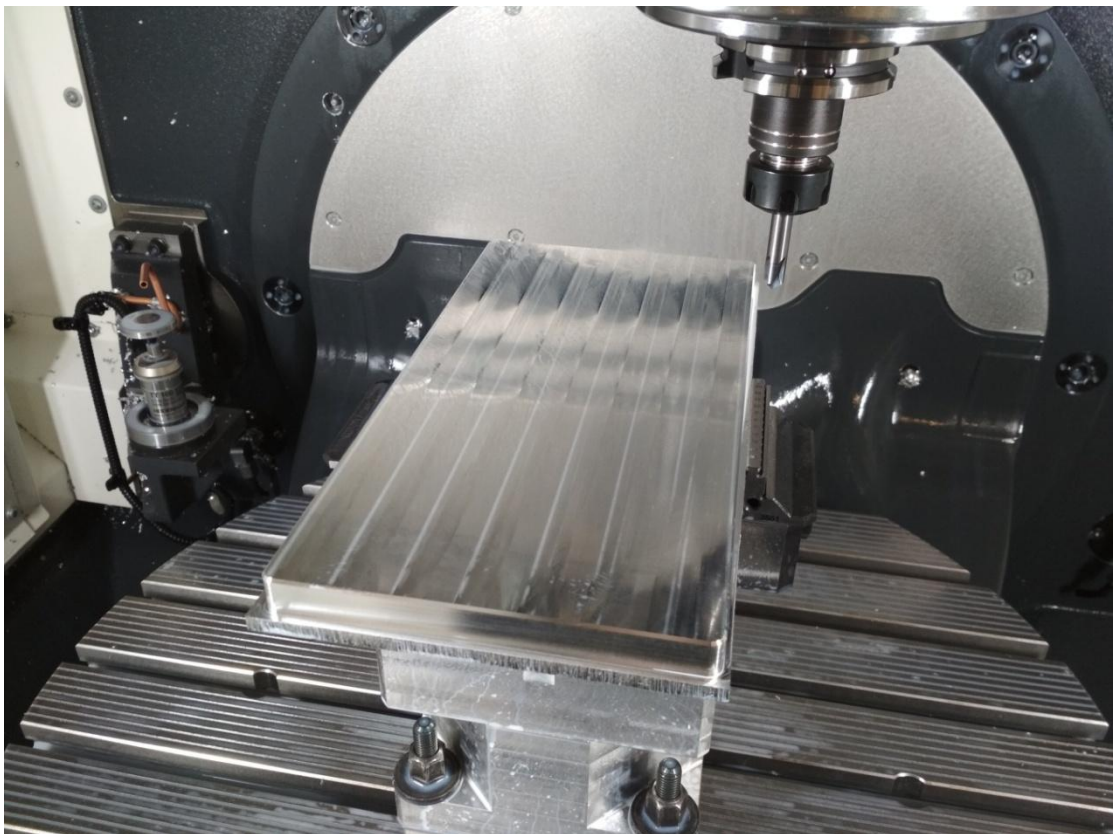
Upnutí polotovaru základní upínací desky a hledání nulového bodu obrobku pomocí sondy.
